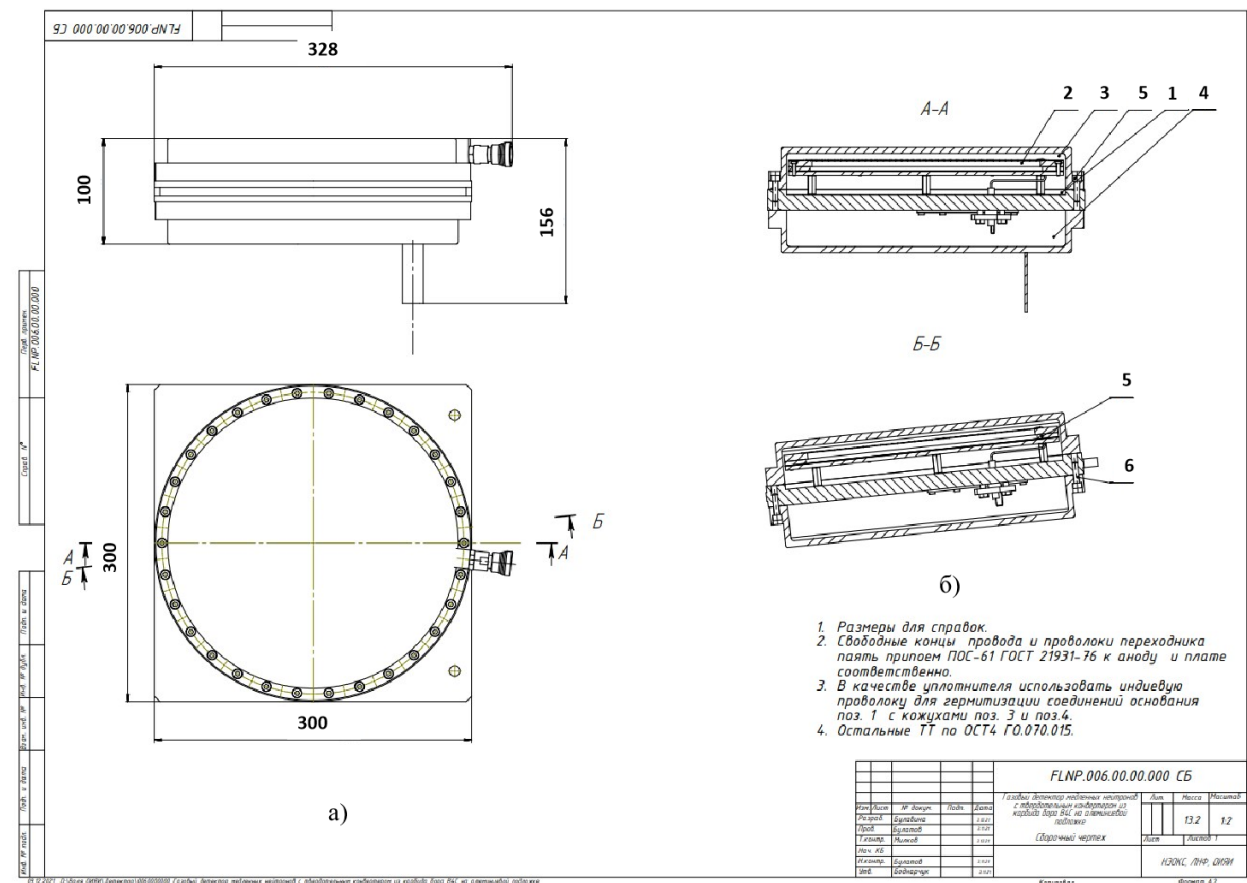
Газовый детектор медленных нейтронов с твердотельным конвертером В₄С на алюминиевой подложке: а) Внешний вид детектора - корпус (кожух) - материал АМГ6; б) Разрез детектора: 1. Платформа; 2. Детектор с твердотельным конвертером из В₄С на алюминиевой подложке и анодная плоскость; 3, 4. Корпус (кожух).
